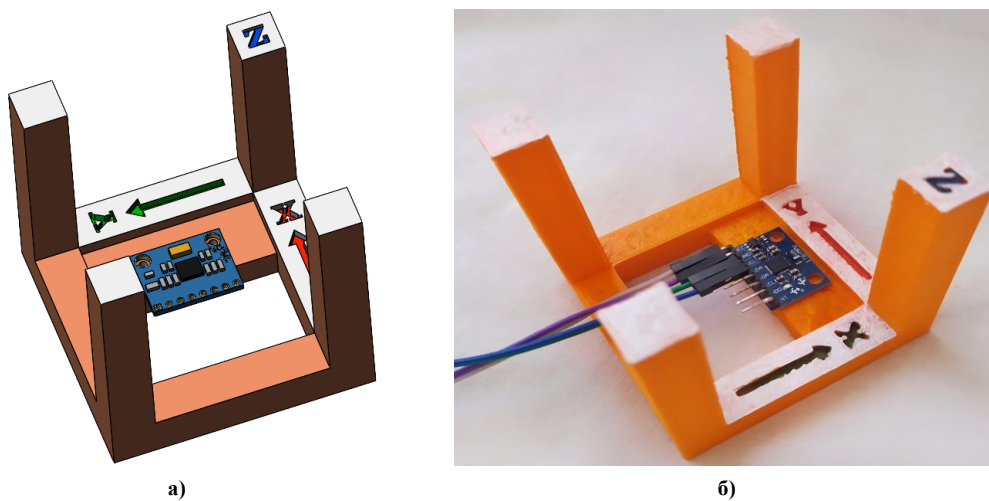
Калібрувальний куб: а) 3D-модель; б) – готовий виріб
